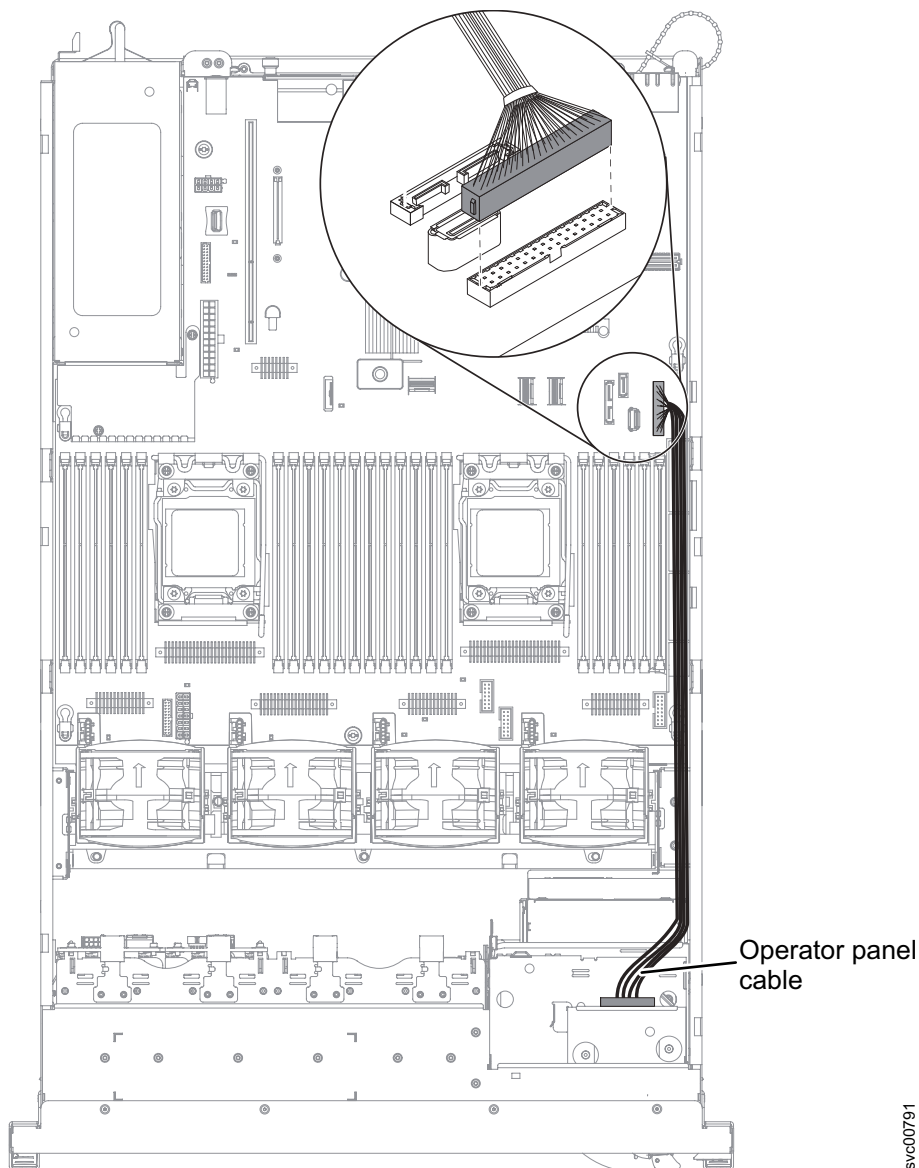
Removendo o cabo do painel de informações do operador do 2145-DH8
